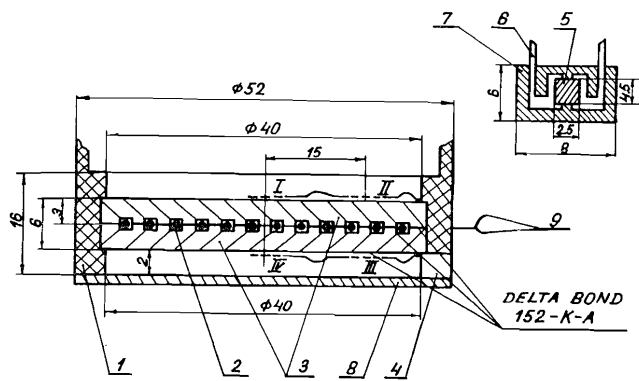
Конструкция экспериментального образца: 1 — обойма из фторопласта, 2 — нагреватель, 3 — экспериментальный образец, 4 — канал для циркуляции гелия, 5 — германий, 6 — серебро, 7 — слюда, 8 — нержавеющая пластина, 9 — провода, I, II, III, IV — термометры.
